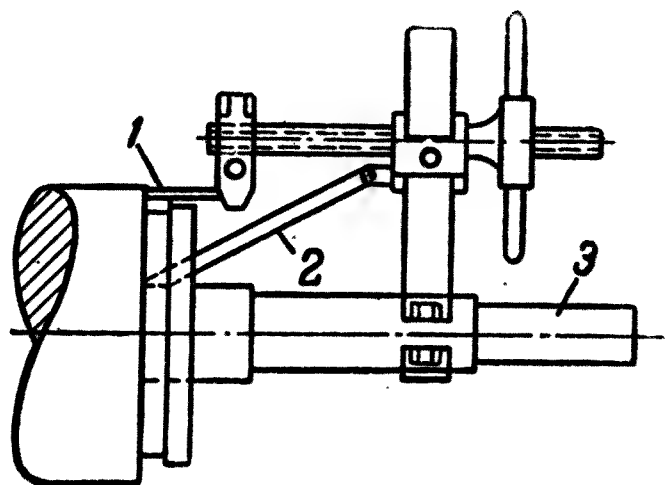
Приспособление для вытаскивания роторных стержней.
